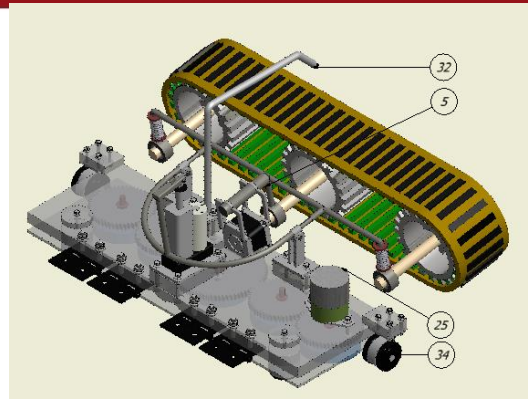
Detalle para rodaje vertical, vista isométrica
